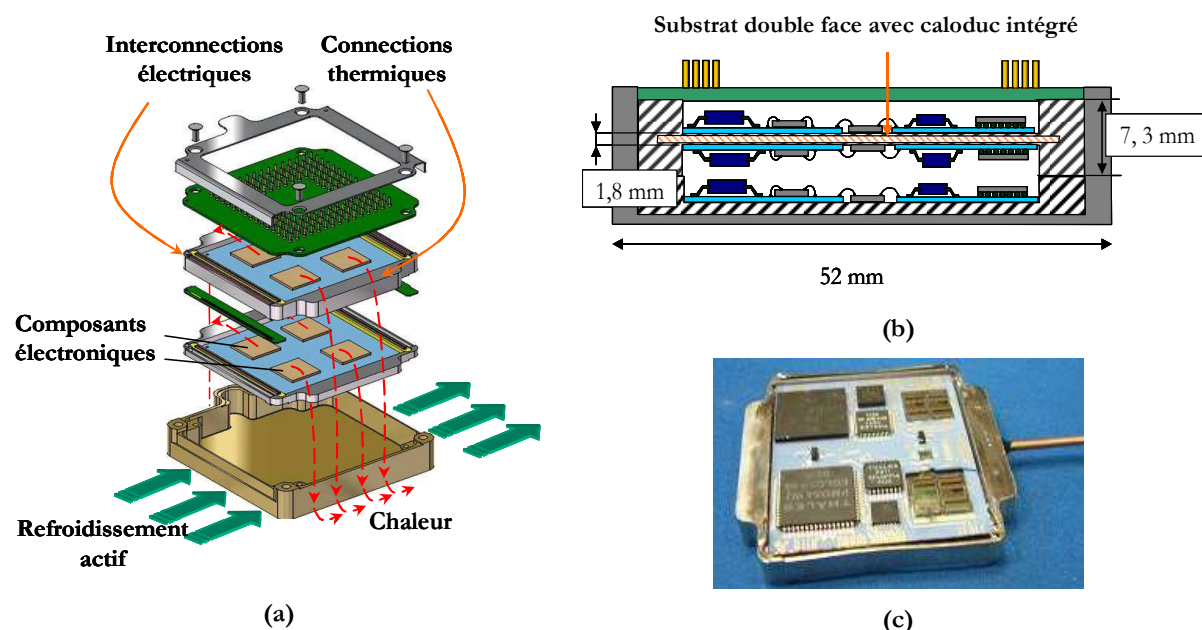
Packaging 3D étudié : (a) Packaging 3D ; (b) Placement du substrat double face dans le packaging 3D; (c) Photo d'un prototype du substrat équipé de caloduc [POP]
